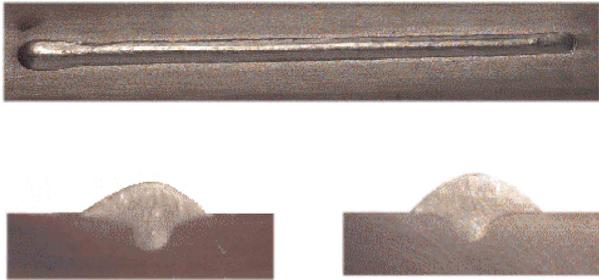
Nahtaussehen bei einer Kontaktrohrabstandsänderung von 8 auf 35mm. Durch die exakte Lichtbogenlängenregelung treten kaum Schweißspritzer auf.
